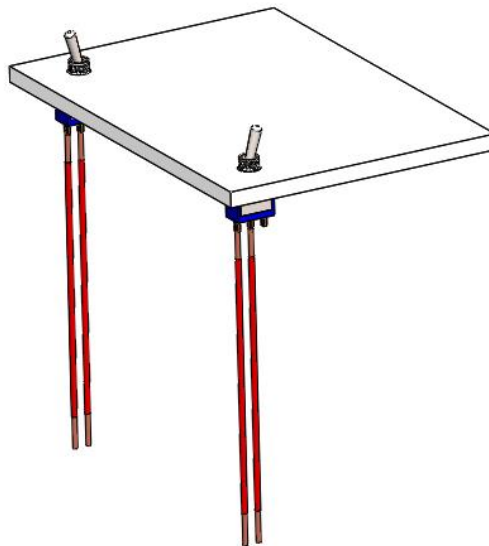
Ensamblaje de los interruptores en el techo del carro autónomo.
